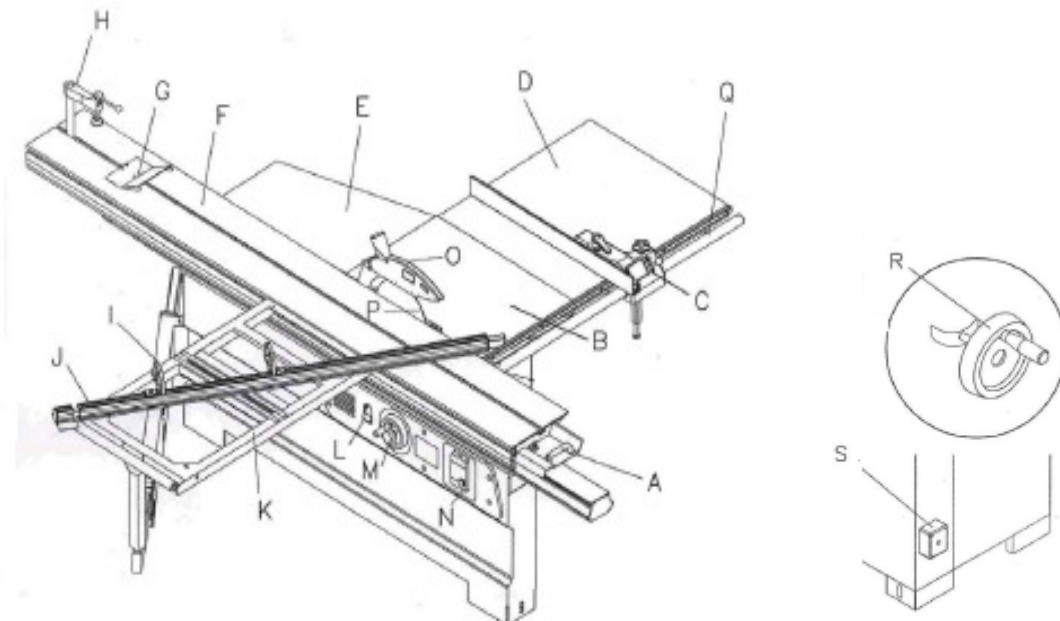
Componentes Escuadradora. . Fuente: Manual de Parte Felder
